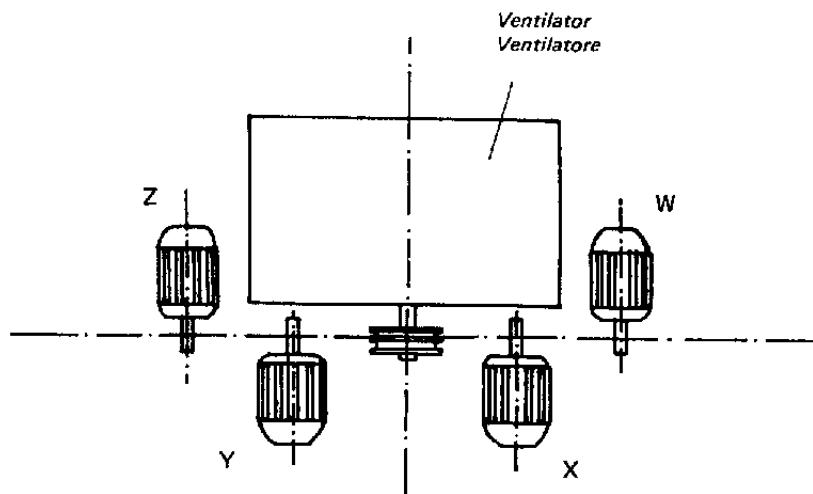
Bezeichnung der verschiedenen möglichen Lagen eines Motors für Riemen- oder Kettenantrieb in der Ansicht senkrecht auf die Befestigungsebene
